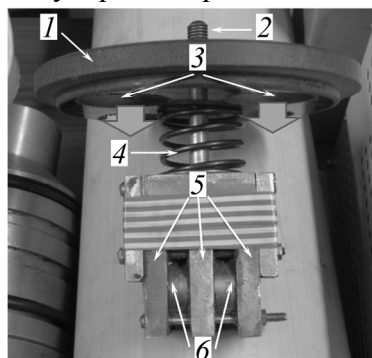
Модульный магнитный фиксатор: 1 — крепежный диск; 2 — шток; 3 — отверстия для подачи воздуха в рабочую камеру; 4 — демпфер; 5 — магнитопроводы; 6 — магниты
